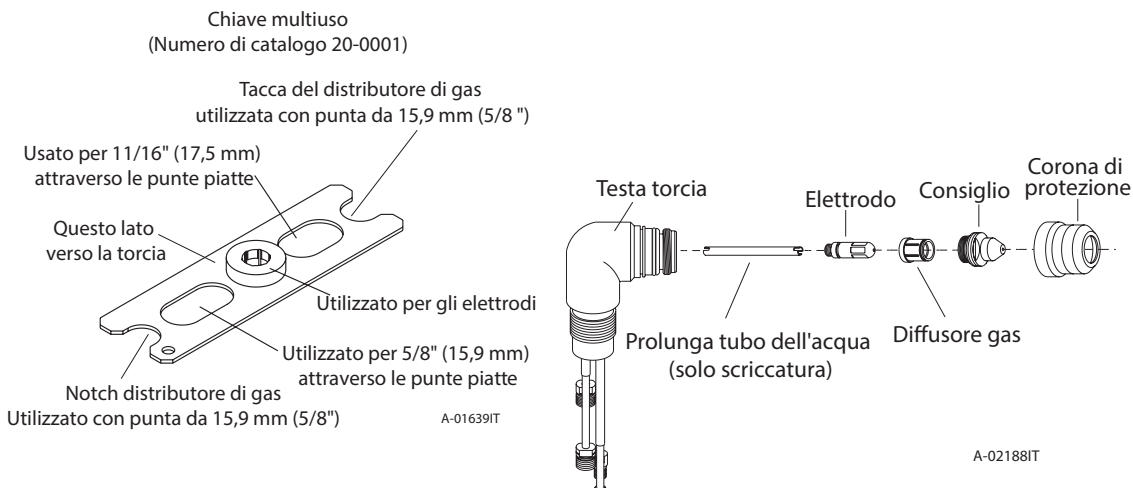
Smontaggio della chiave multiuso e del distributore di gas
